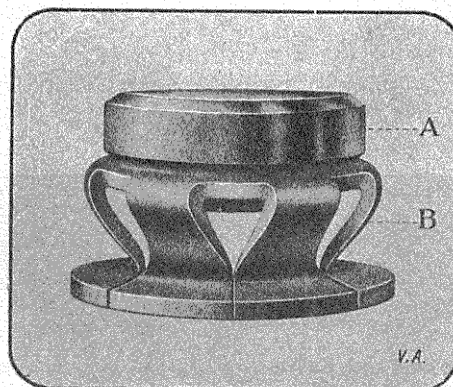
Le Rivet de l'Antidérapant Palmer.
